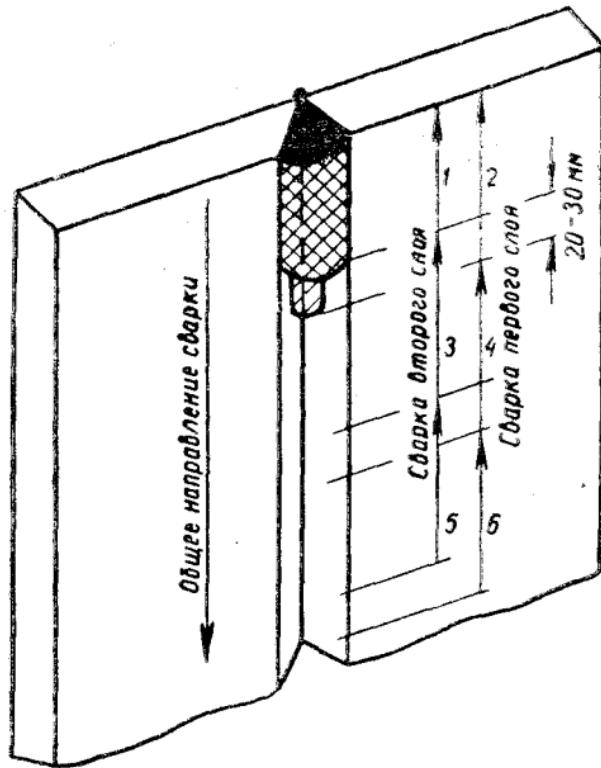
Схема сварки обратноступенчатым способом в два слоя. Цифрами и стрелками показаны очередьность и направление сварки
